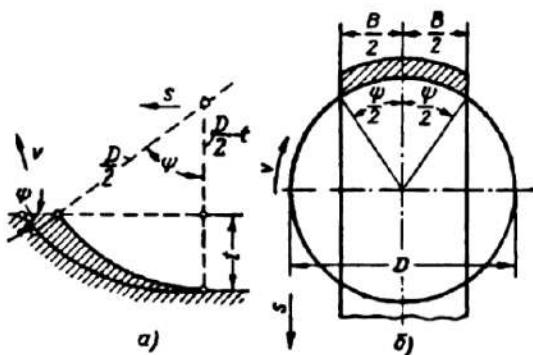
Ширина и глубина фрезерования для основных типов фрез.
